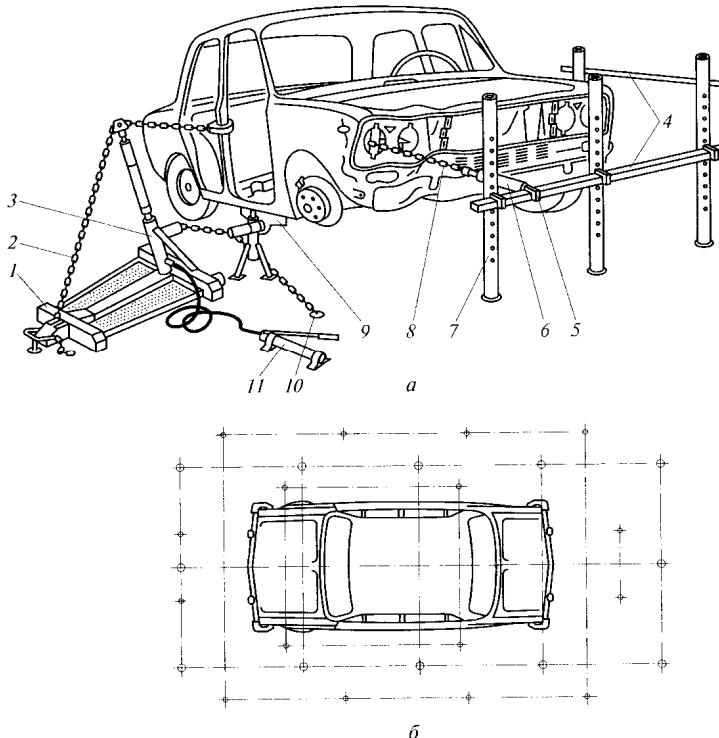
Стенд для правки кузовов с анкерными устройствами (а) и схема расположения анкеров и гнёзд под вертикальные опоры (б): 1 – силовая установка; 2 и 8 – цепи; 3 и 6 – силовые цилиндры; 4 – поперечные траверсы; 5 – ползушка; 7 – переносные вертикальные опоры; 9 – силовая поперечная труба; 10 – анкерное устройство; 11 – гидравлический насос
